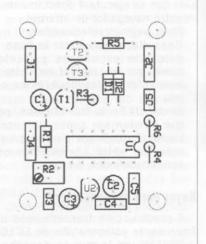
Placa de circuito impreso para el keyer y disposición de los componentes.
